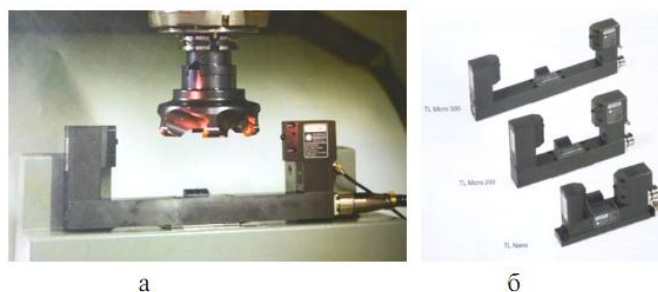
Лазерні системи вимірювання інструментів TL: а – на верстаті під час вимірювання; б – конструкції для різних розмірів інструменту
